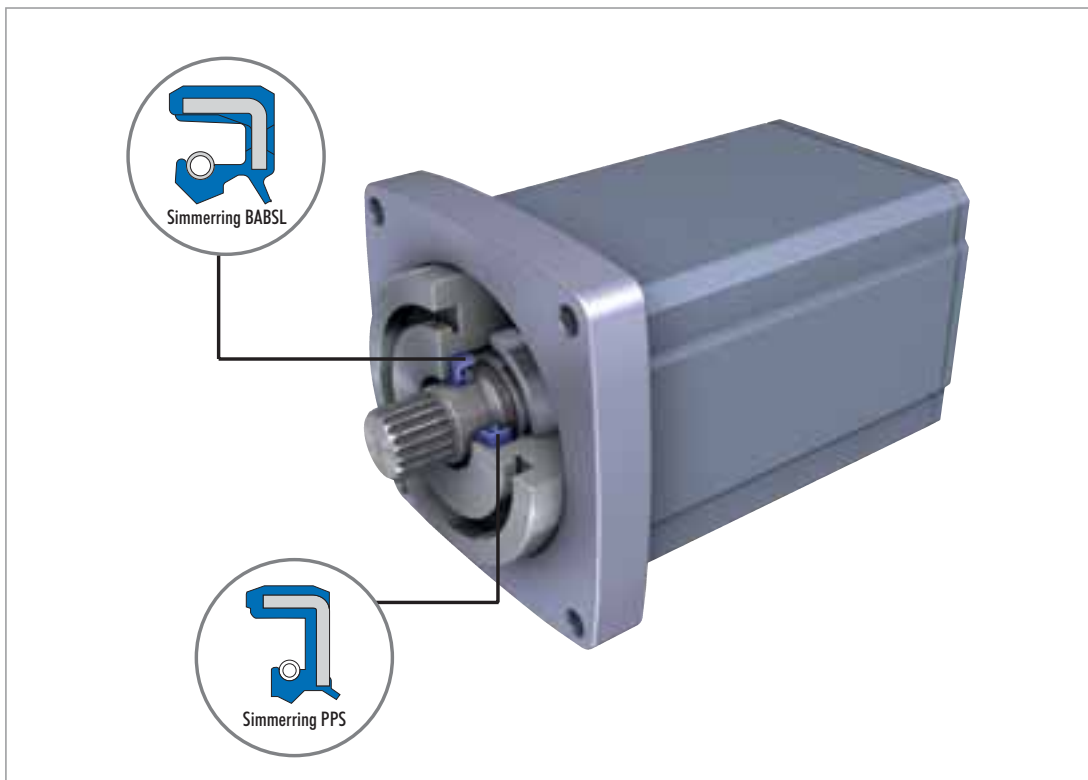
Drehdruckbelastbare Simmerringe in hydraulischen Pumpen und Motoren
